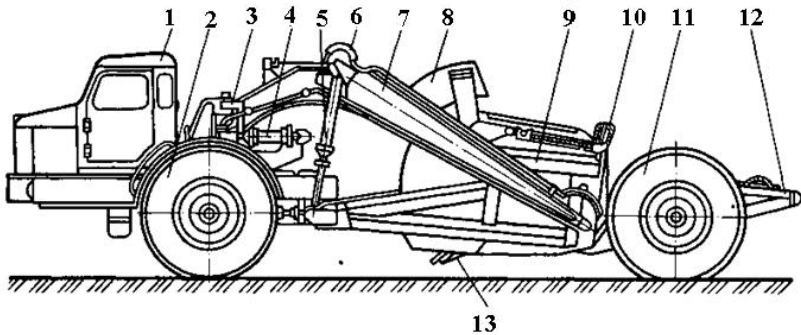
Конструктивна схема напівпривісного скрепера [9]:
